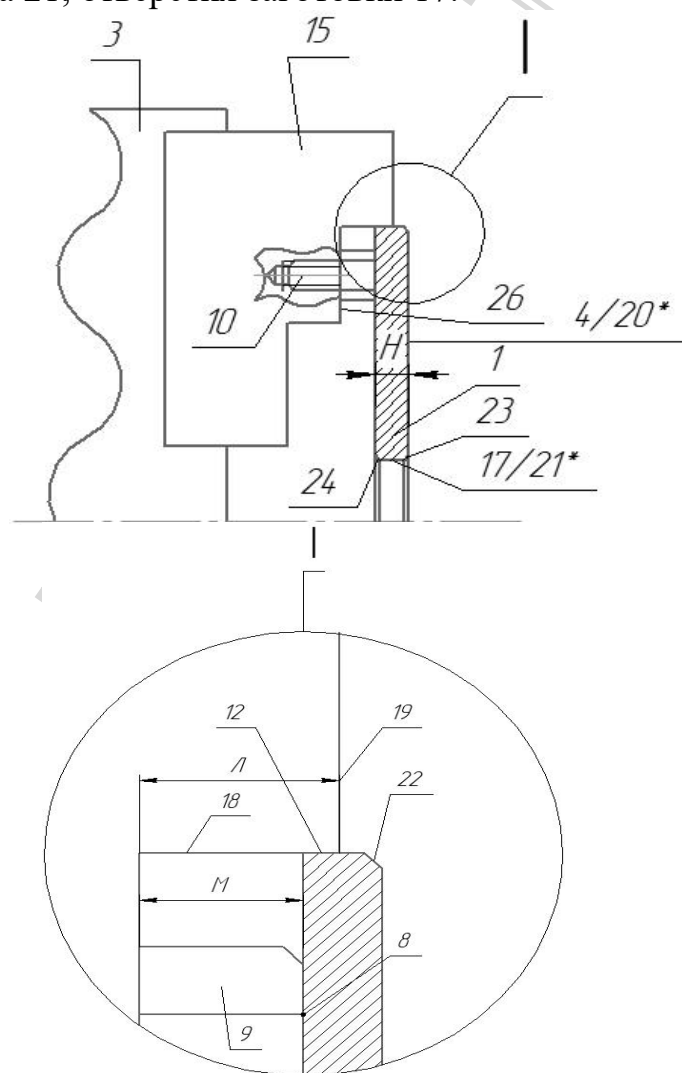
Схема второй токарной операции обработки заготовки фланца
